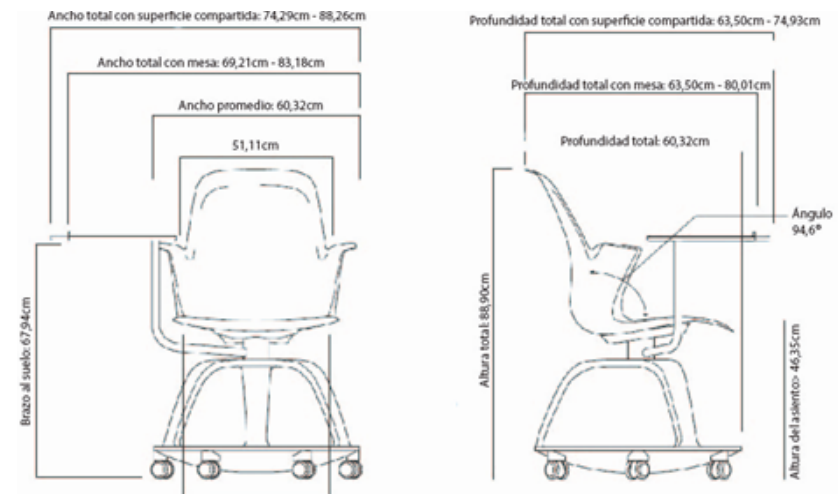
Planimetría del mobiliario. “Silla Node 480 Series”, Steelcase, 2015
